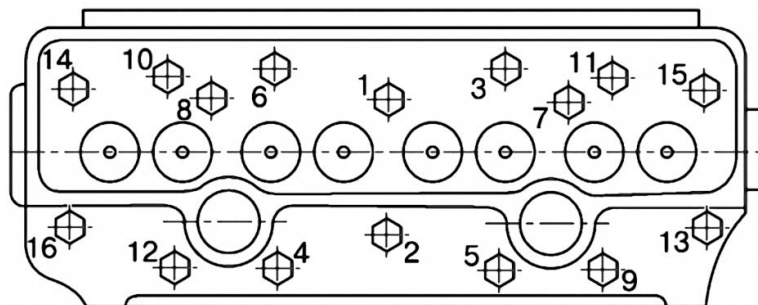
Схема последовательности затяжки болтов крепления головки цилиндров двигателя Д-245
